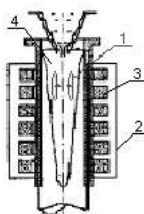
Схема электромагнитного перемешивателя, совмещенного с кристаллизатором: 1 – направление движения расплава; 2 – магнитопровод; 3 – обмотка индуктора; 4 – жидкая фаза слитка
